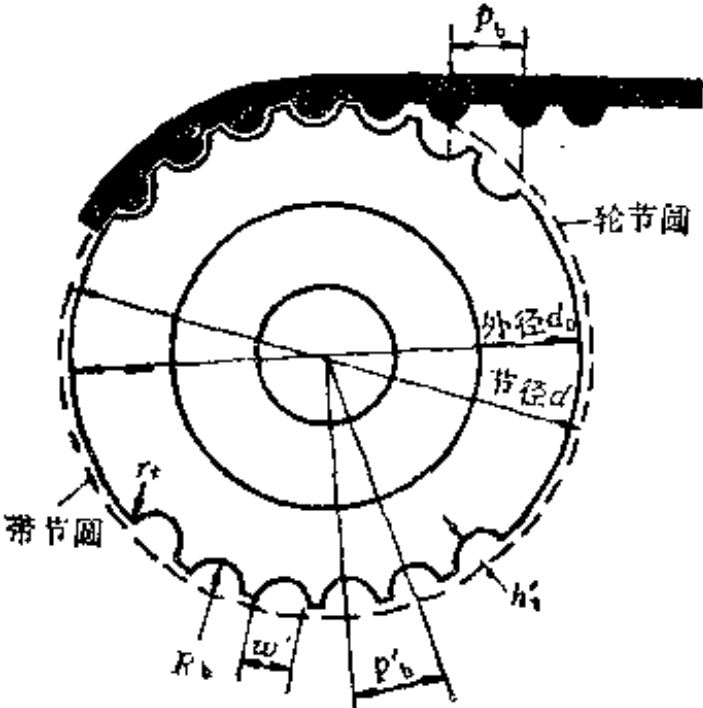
圆弧形齿带轮的齿形尺寸 符号位置
